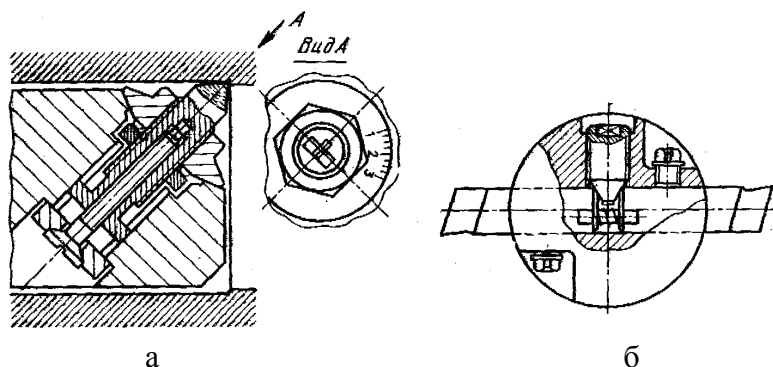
Різучий інструмент для обробки отворів:
